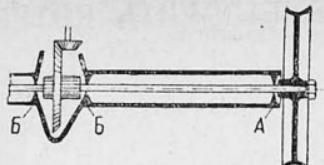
Схема нагруженной полусоси. А — подшипники колеса; Б — подшипники ведомой шестерни главной передачи
